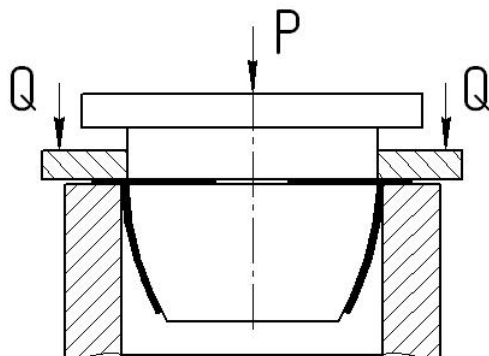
Схема отбортовки в инструментальном штампе тонкостенных заготовок
